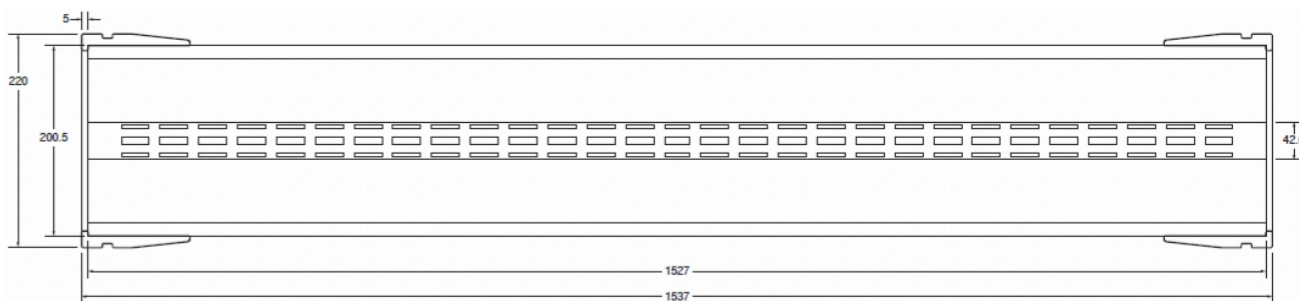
Габаритные размеры ZW700B-8060A (мм)
